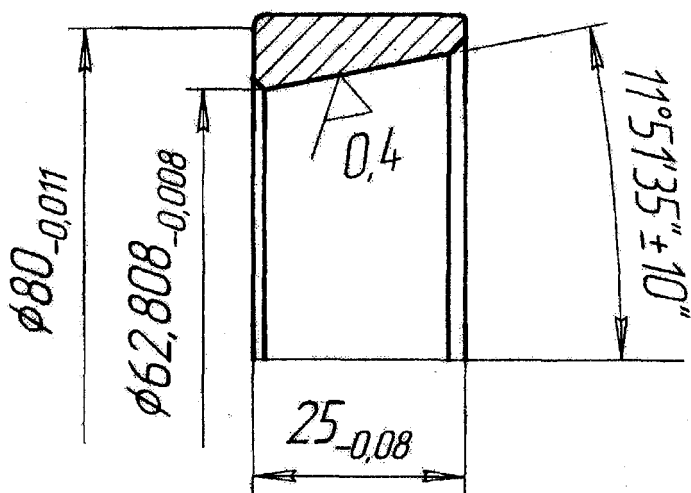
Операционный эскиз детали наружного кольца подшипника 6-7607AY
